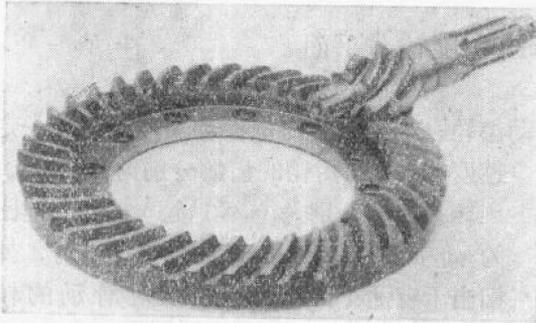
跃进-130 载重汽车螺旋锥齿轮
